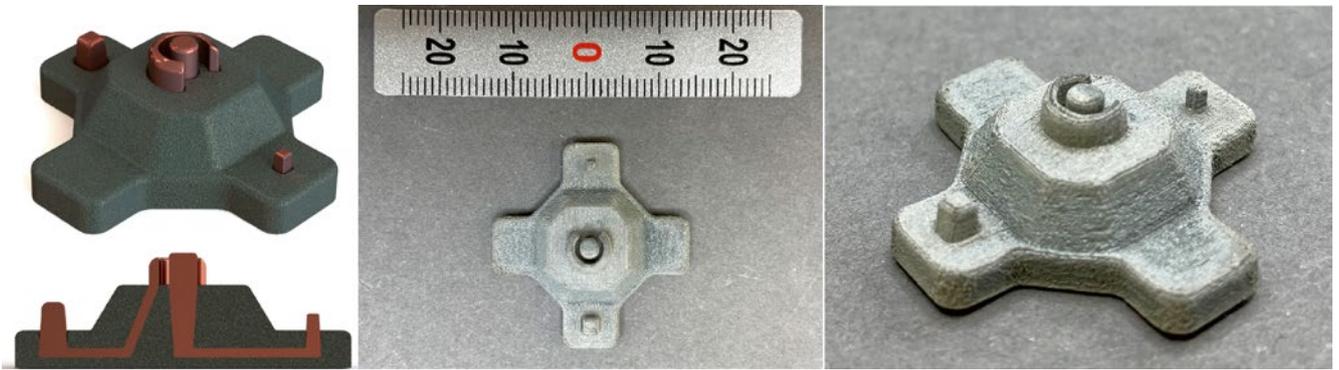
Keramische Zündquelle (links: CAD; Mitte und rechts: co-gesintertes Bauteil). (© Fraunhofer IKTS)
